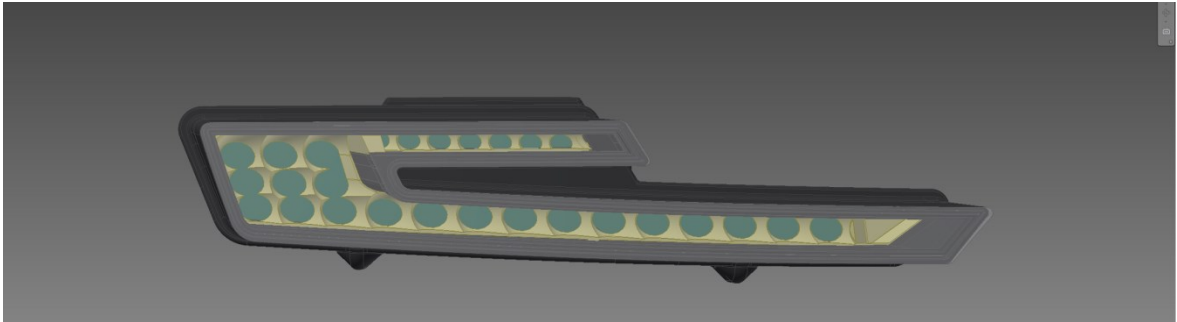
Housing předního světlometu navržený konstruktérem
